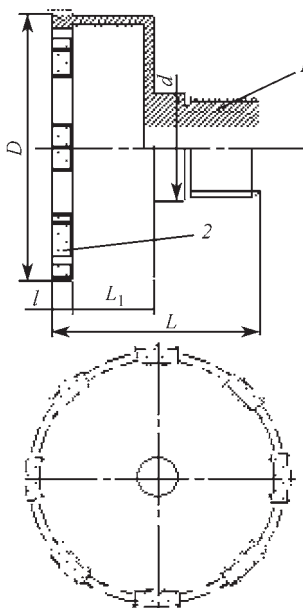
Конструкция алмазно-абразивного кольцевого сверла:
